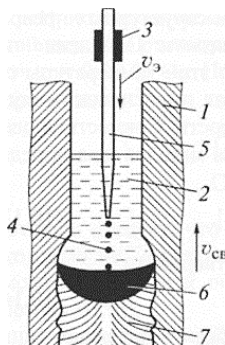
Схема защиты металла при электрошлаковой сварке:
